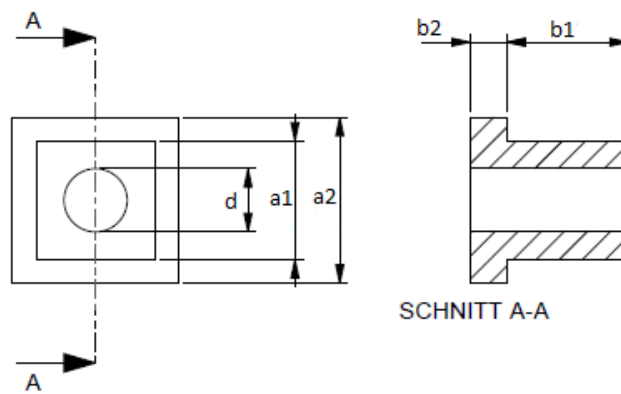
Bemaßungsskizze für die Wellenbuchsen mit quadratischem Querschnitt
